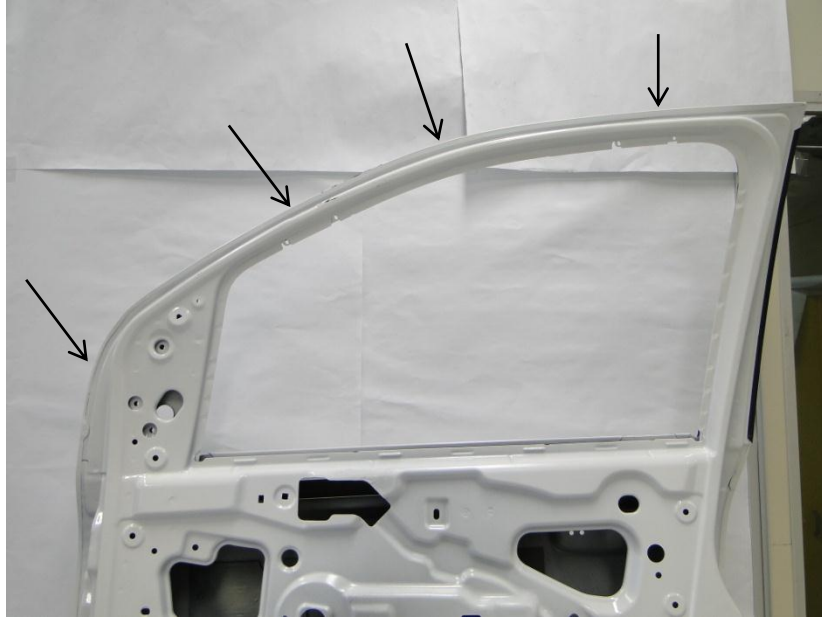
Componente porta. As setas indicam a região perimetral de aplicação do adesivo.
